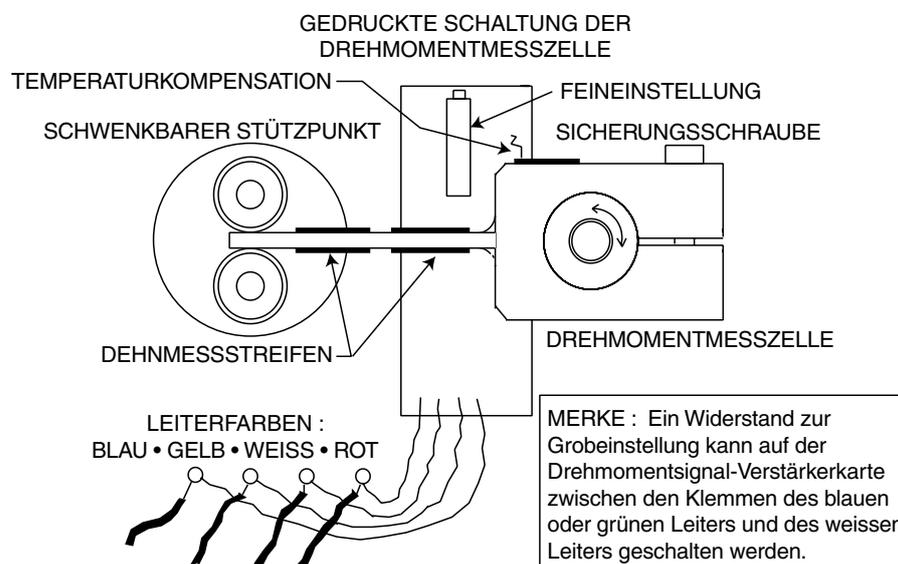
Mechanischer Prinzipaufbau einer Drehmomentmesszelle
